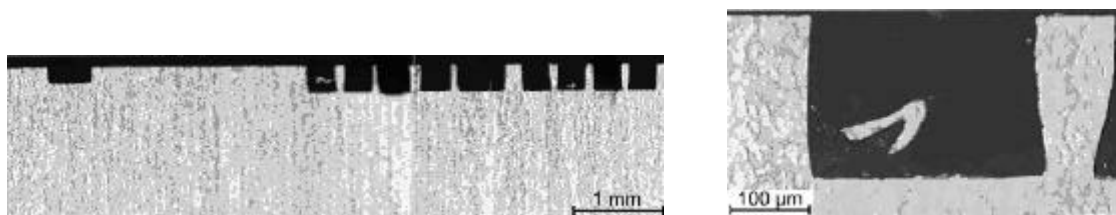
Profilschnitt einer mikrogefrästen Werkzeugstruktur
